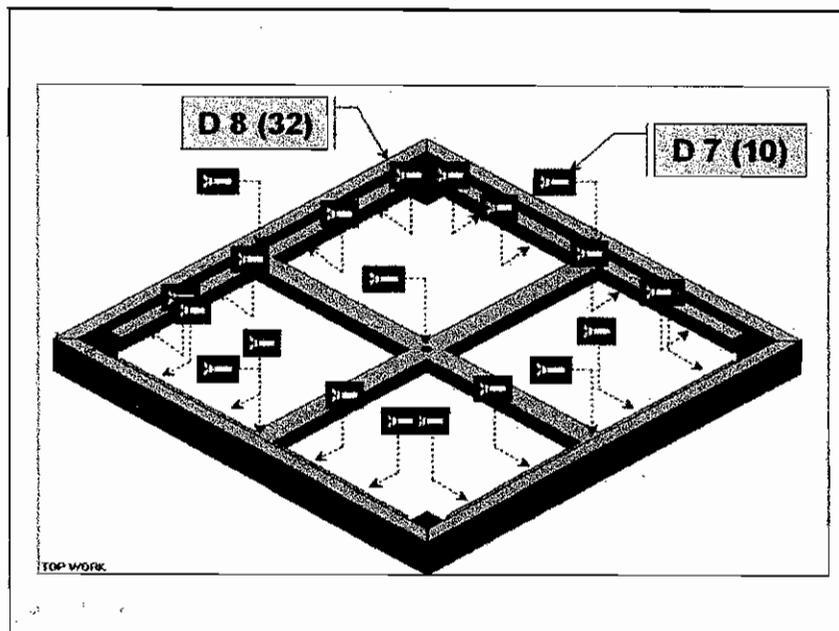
Assembly drawing ของโต๊ะพับแบบถอดประกอบได้ (1)
